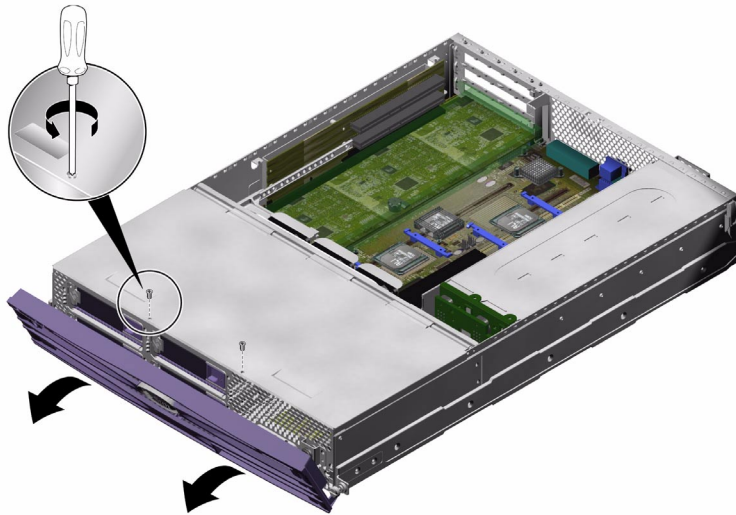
Emplacement des vis de la section avant du couvercle
